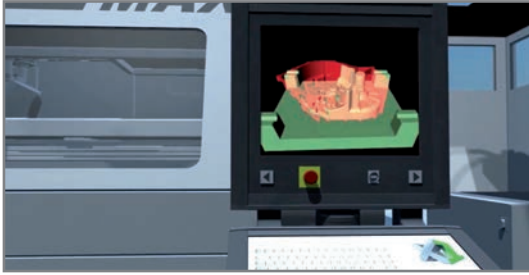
Die Daten für die Sandform des Gussteils werden auf die 3D-Sanddruckmaschine geladen.
